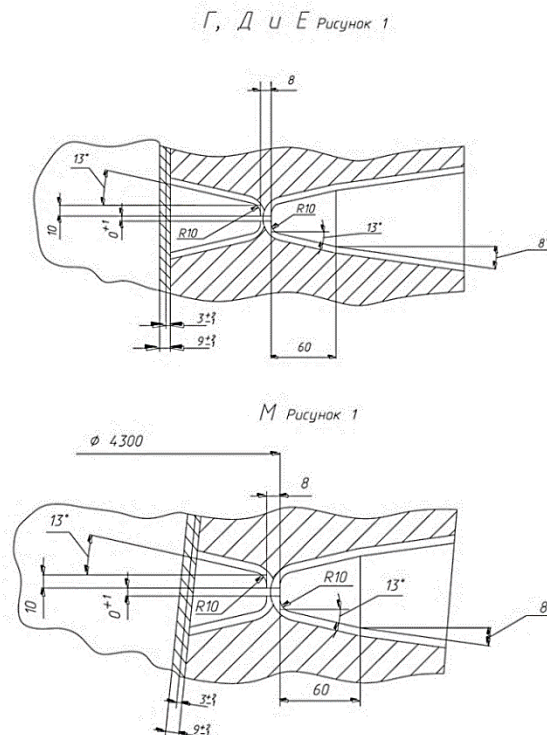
Сварные соединения обечаек корпуса реактора ВВЭР-1200
